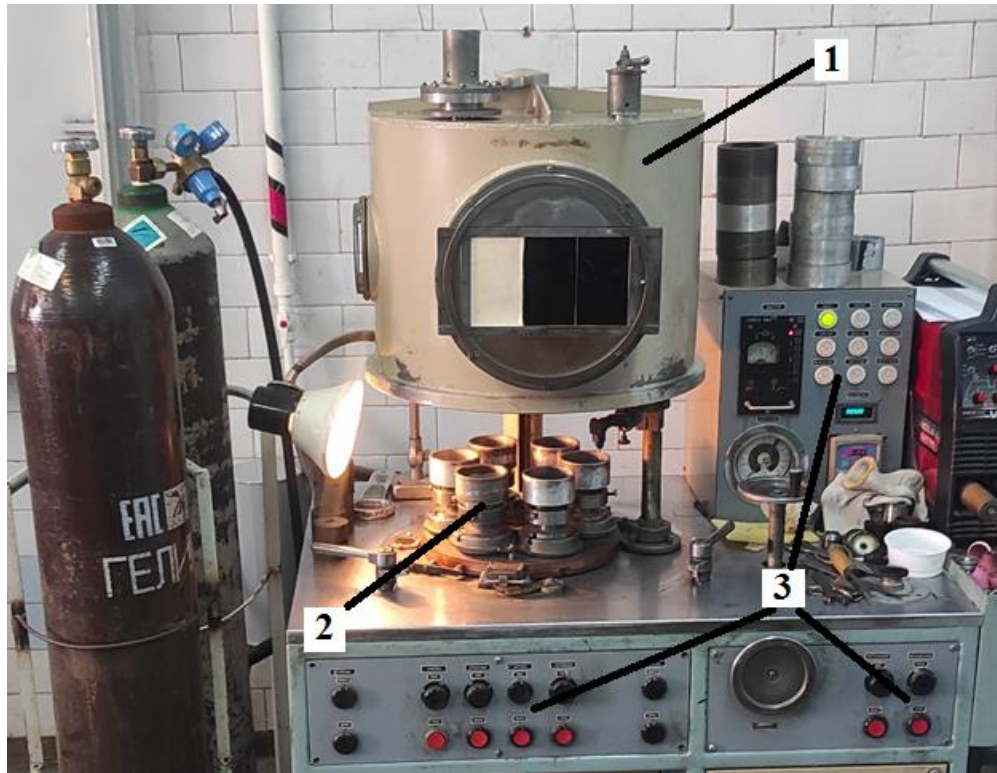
Установка аргодуговой сварки карусельного типа
